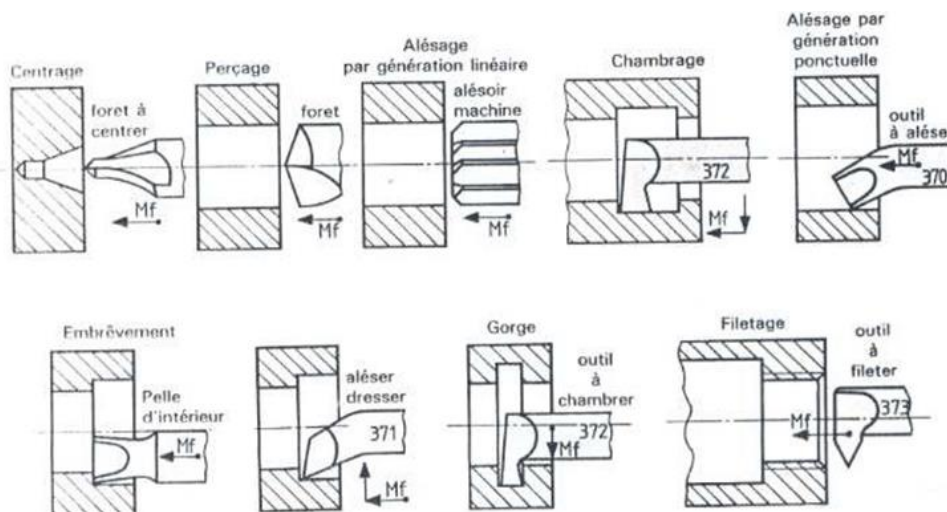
Des outils de forme, des outils rotatifs [3]
